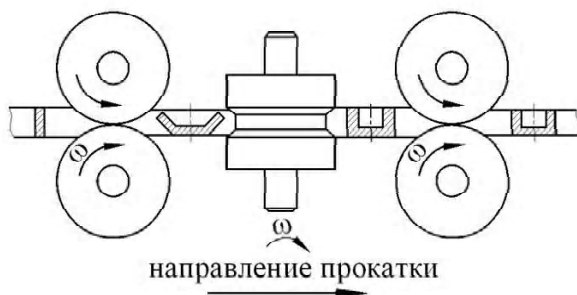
Схема прокатки профильной полосы на непрерывном трехпарном стане 280
